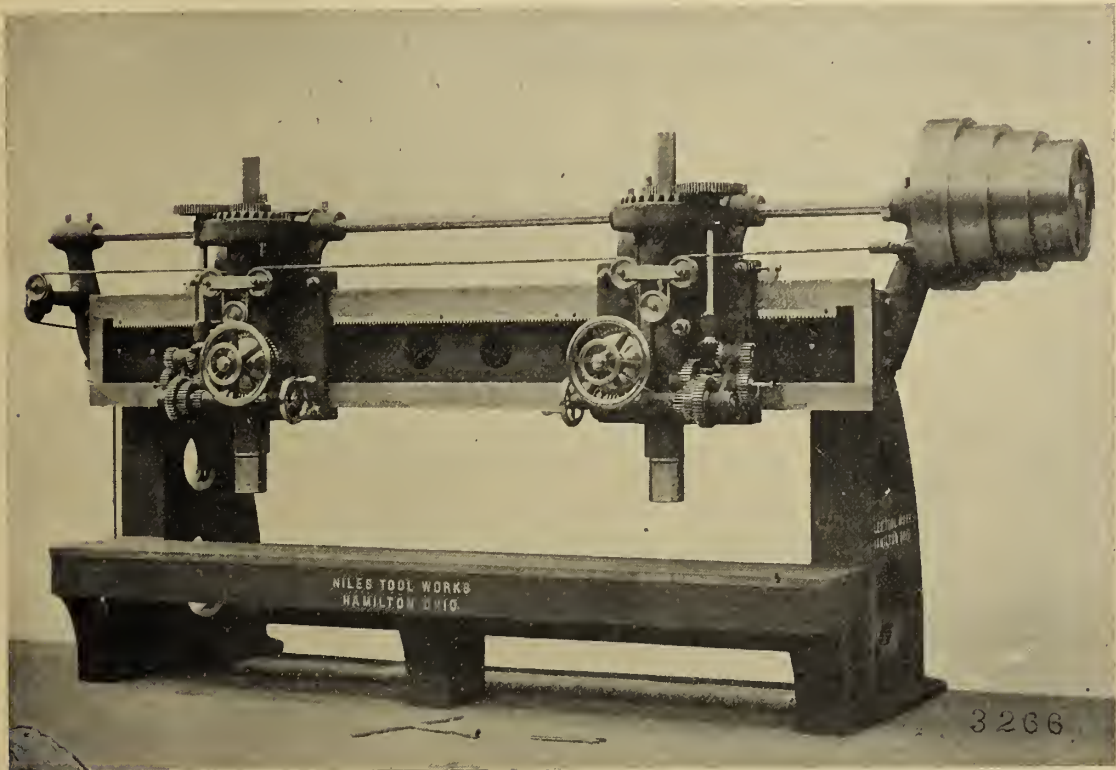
Machine à aléser les bielles type des *Niles Tools Works*.
